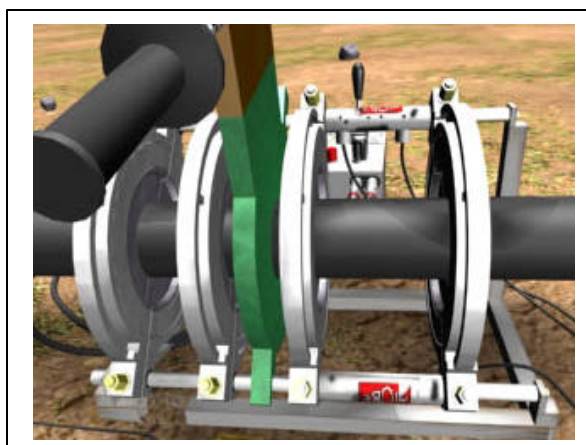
Formado o cordão, a pressão de solda e o contato da placa com os tubos deverão ser mantidos pelo tempo recomendado pelo fabricante do equipamento.
